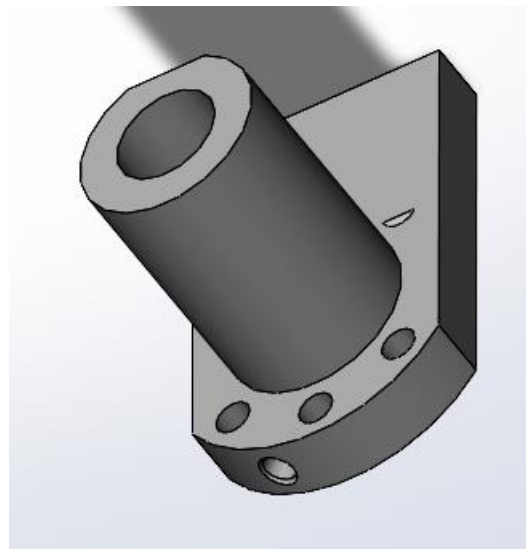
Widok po skosie obrazujący element mechanizmu śrubowo-tocznego – uproszczony prawy silnik.
